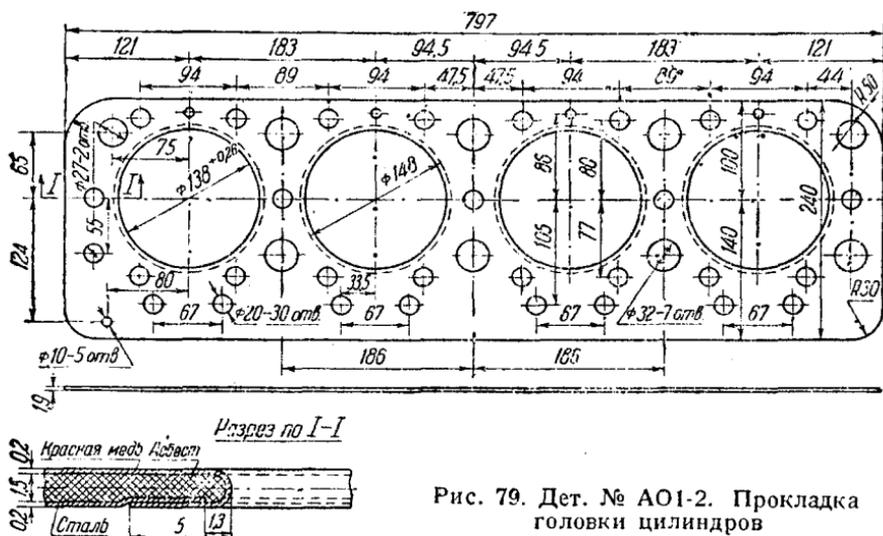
Дет. № АО1-2. Прокладка головки цилиндров
